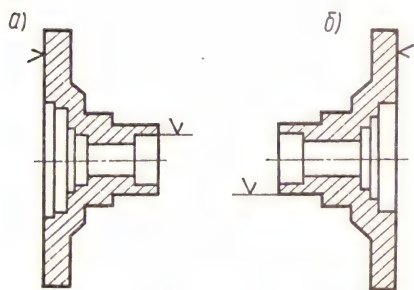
Схема базирования при обработке цилиндрической поверхности:
